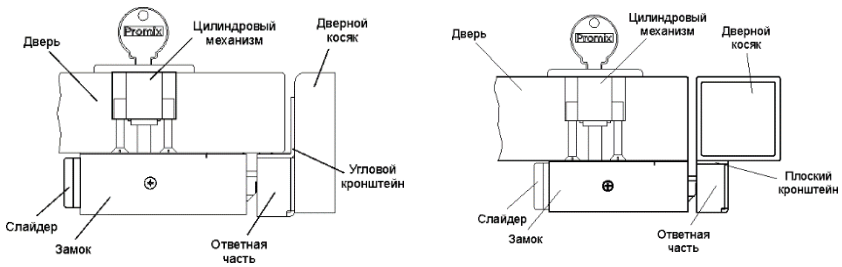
Монтаж замка на дверь открывающуюся наружу
